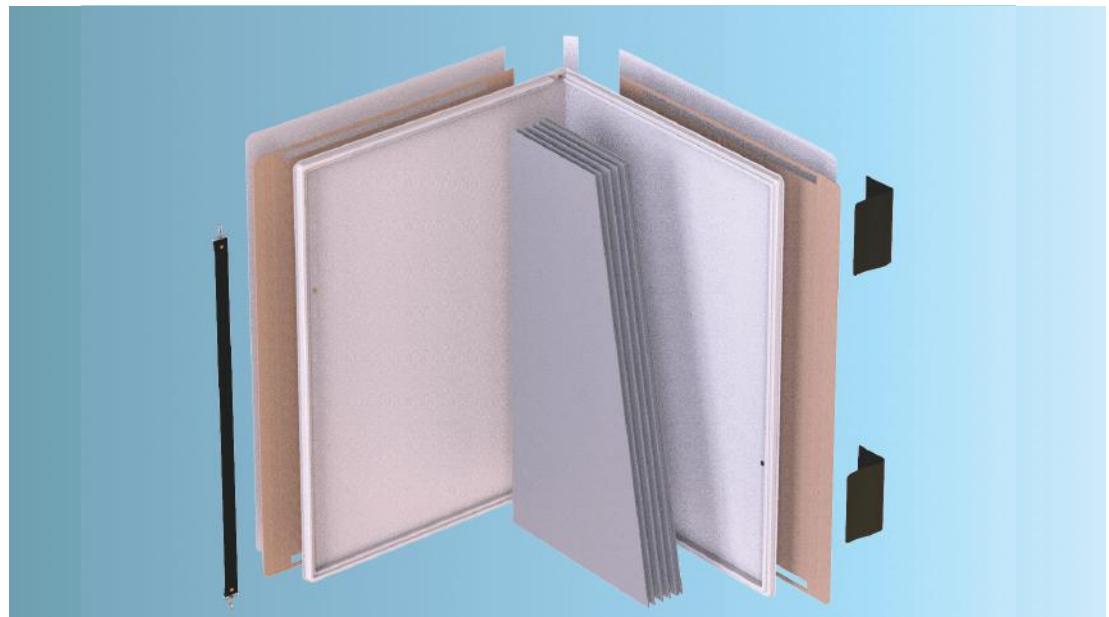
Explodido do caderno. Fonte: elaboração própria.
